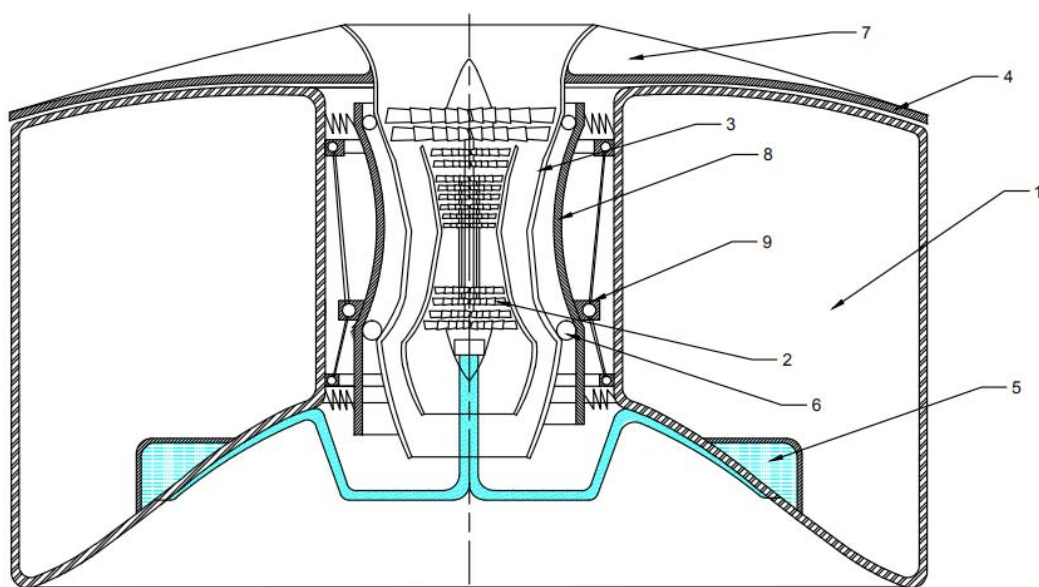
Схема ЛА с поворотной пластиной (1 – корпус ЛА, 2 – ТРД, 3 – наружная обечайка, 4 – вращающийся диск, 5 – топливная ёмкость, 6 – подшипники, удерживающие обечайку, 7 – ребро жёсткости диска, 8 – качающаяся гильза, 9 – шарнирно-стержневое крепление гильзы).
